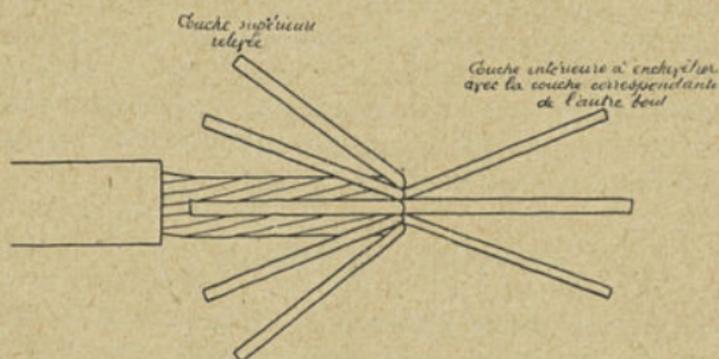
Préparation d'un bout de câble pour une épissure.
